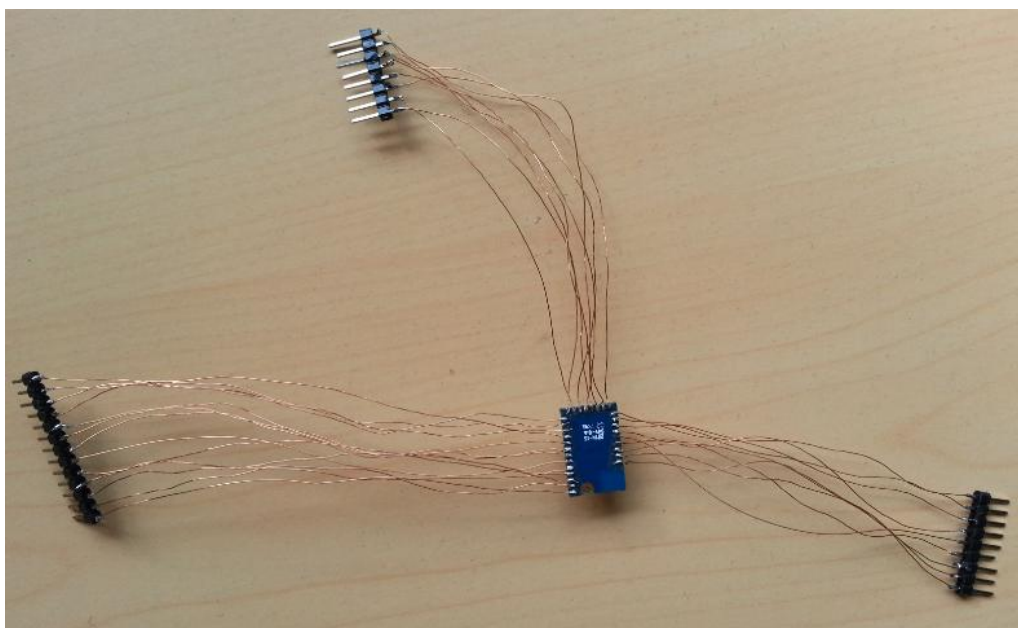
Face arrière du module Bluegiga BLE112 soudé
